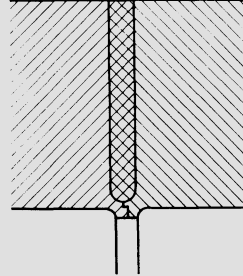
Tulpennut der geschweißten BBC-Rotoren
